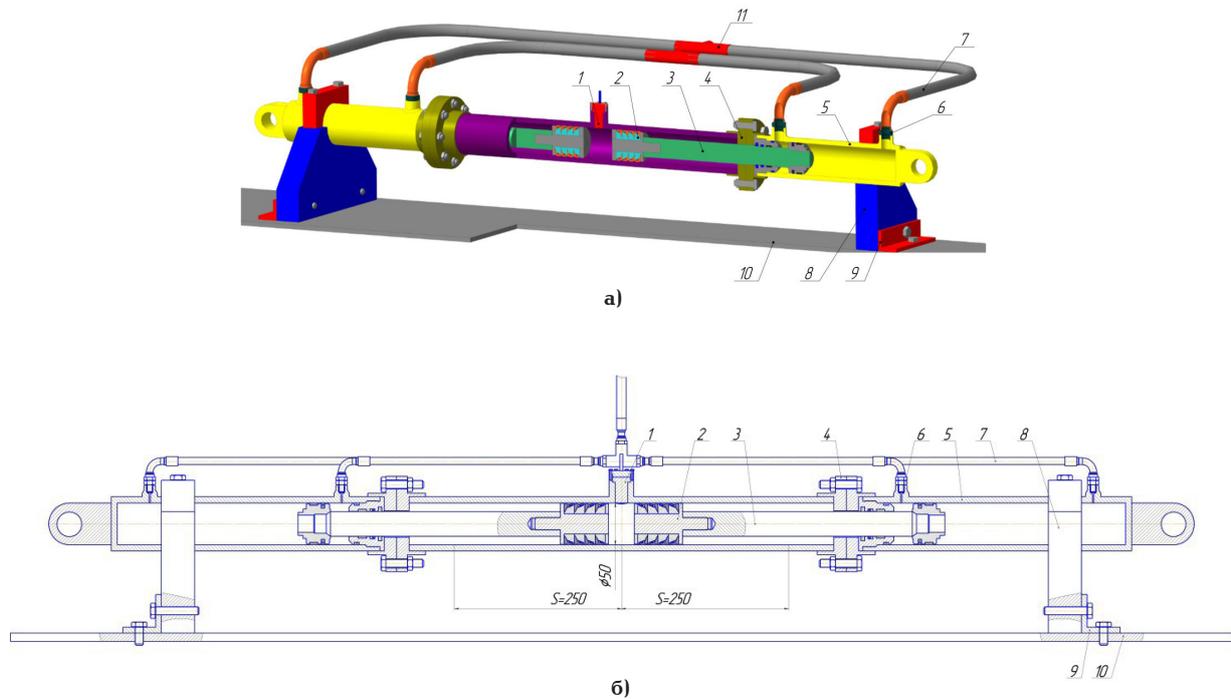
Общий вид конструкции тихоходной ступени с двумя поршнями:
